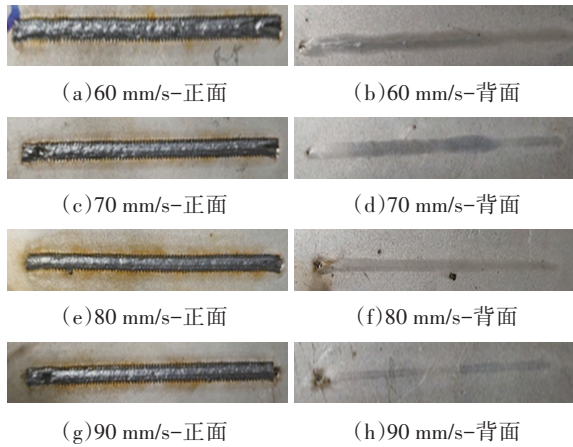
不同焊接速度下正面与背面的焊缝形貌
